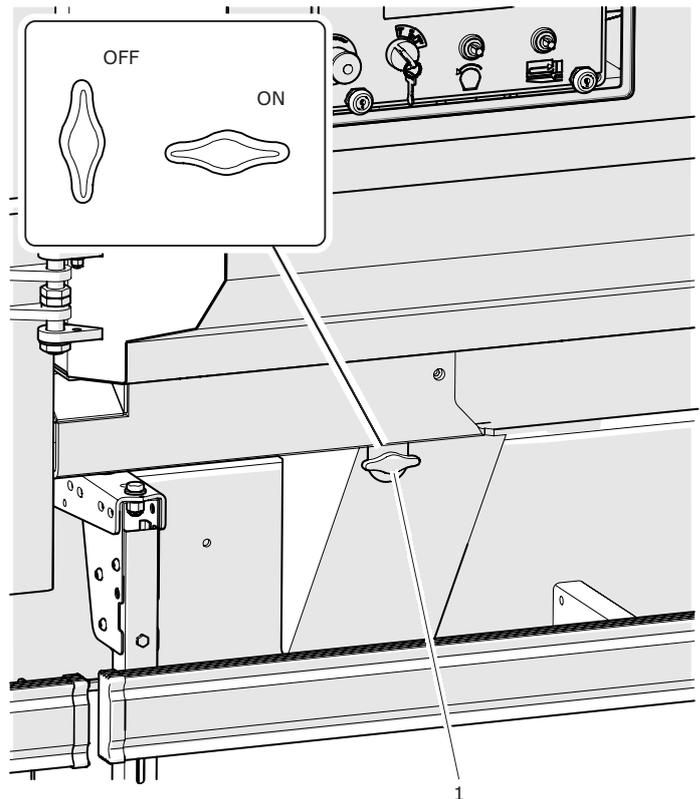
Hauptschalter (3) in die Position (C) bringen – Senken des (1) Schalter
